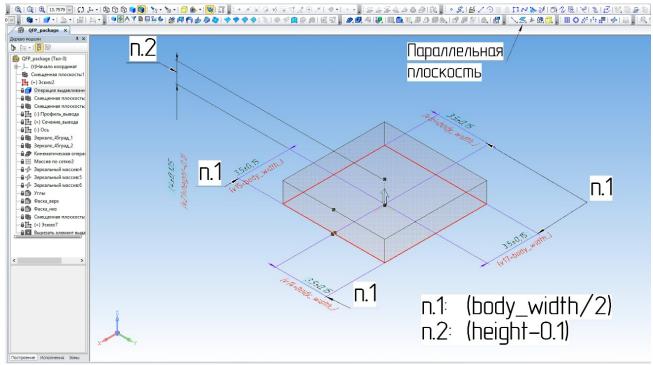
задание объема корпуса QFP и привязка переменных.
